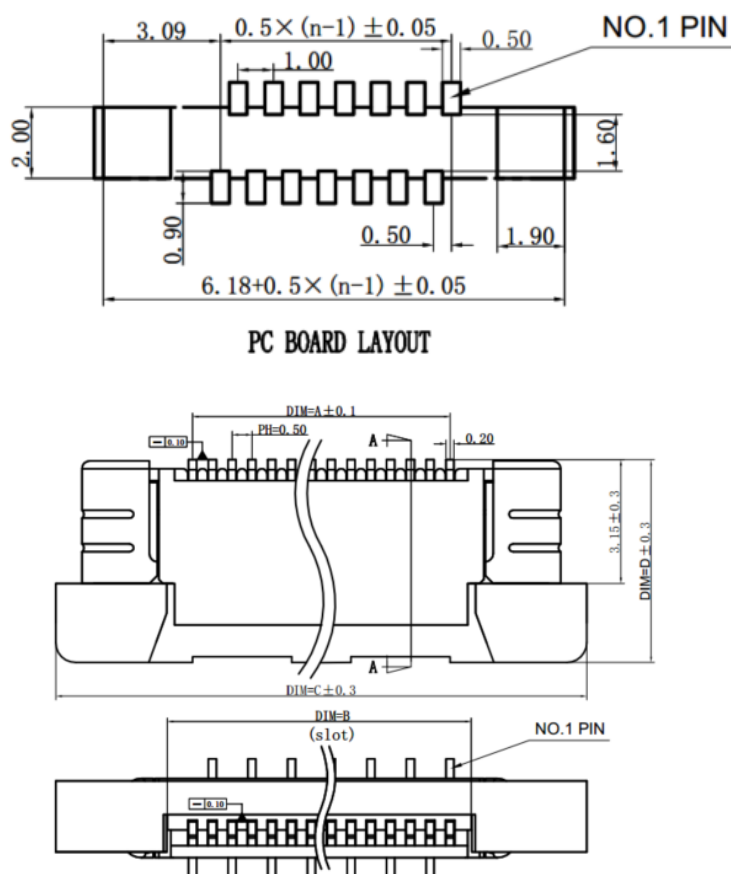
间距 0.5mm 立式双排 30PIN PCB 封装图
